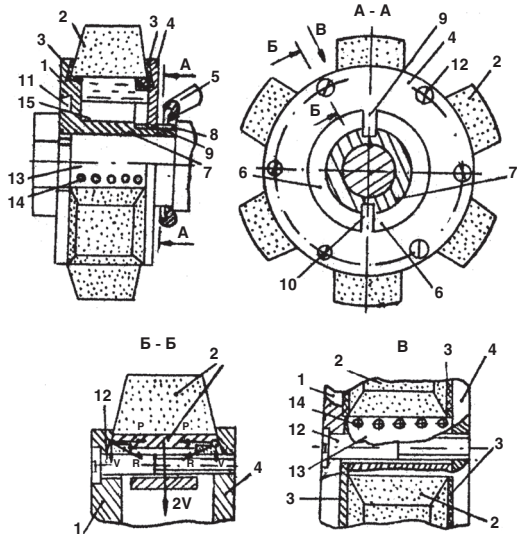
Сборный абразивный круг с креплением режущих сегментов по четырем сторонам: 1 — корпус; 2 — абразивный сегмент; 3 — упругий элемент; 4 — крышка; 5 — трубопровод; 6 — щель; 7 — посадочная втулка; 8 — продольный паз; 9, 10 — радиальные участки; 11 — кольцевая канавка; 12 — винт; 13 — планка; 14 — отверстие; 15 — приемная полость.
